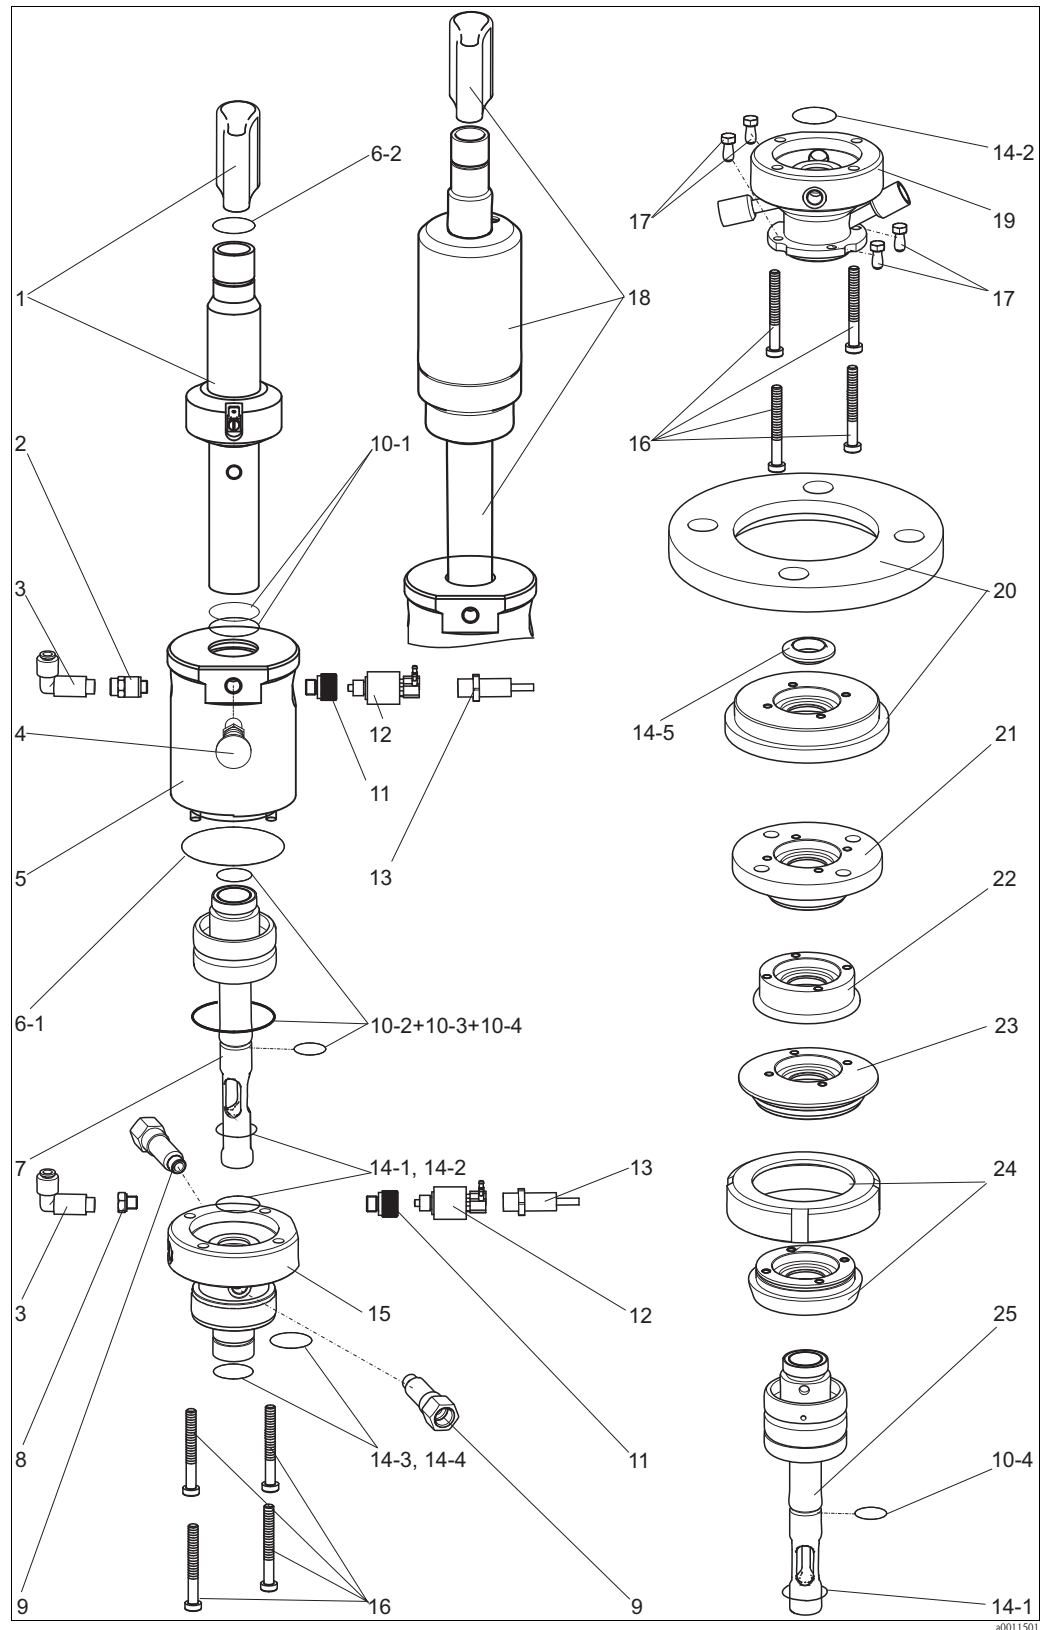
Ersatzteile (alle Armaturenausführungen)
